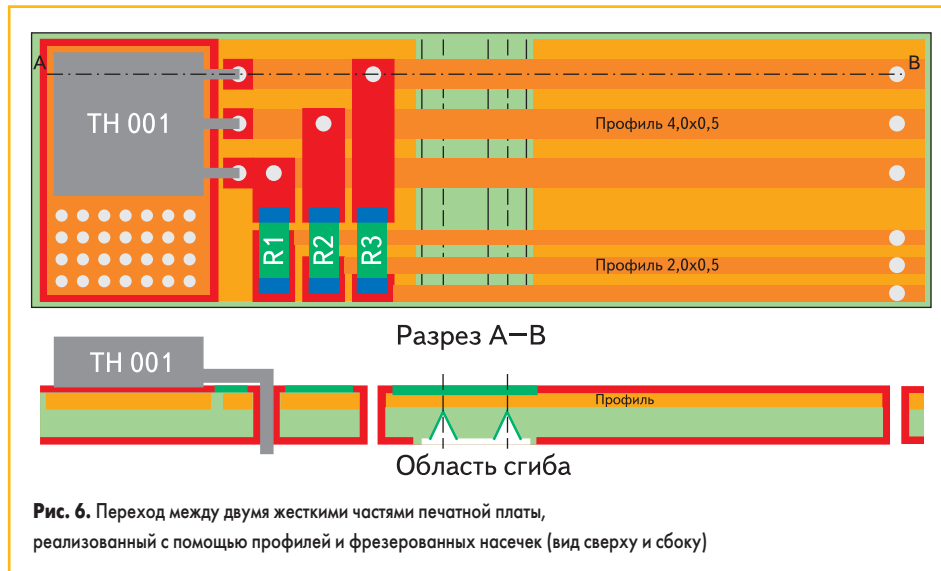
Переход между двумя жесткими частями печатной платы, реализованный с помощью профилей и фрезерованных насечек (вид сверху и сбоку)
